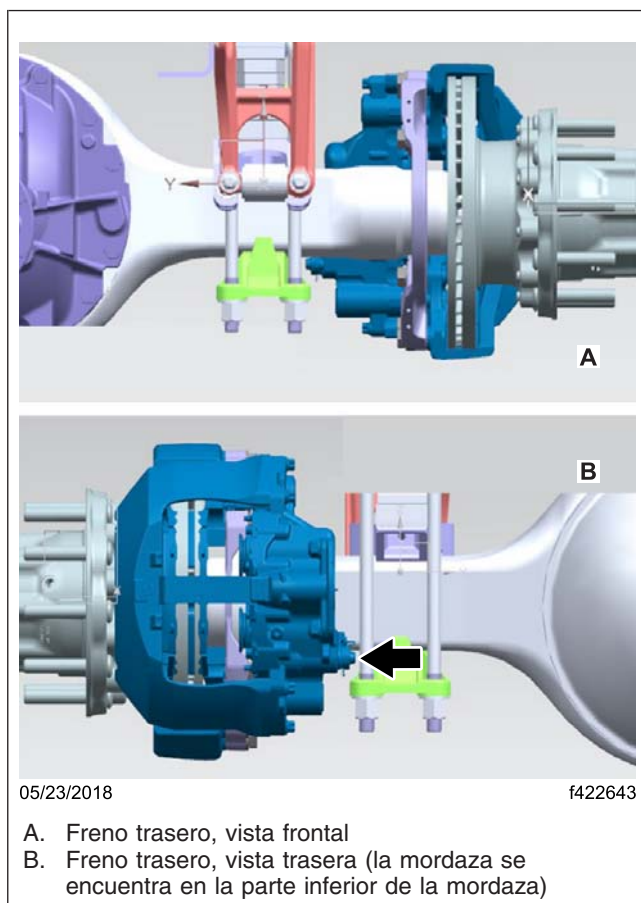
, Posición correcta de la mordaza, lado izquierdo
